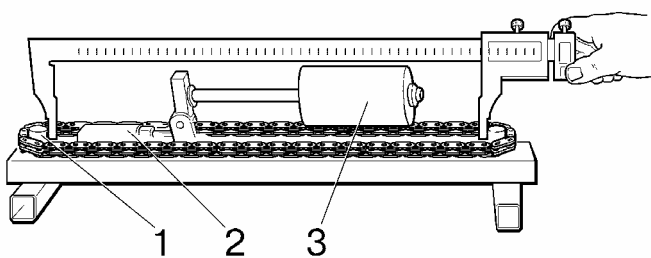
Приспособление 67.7824.9521 для проверки износа (вытяжки) цепи:
